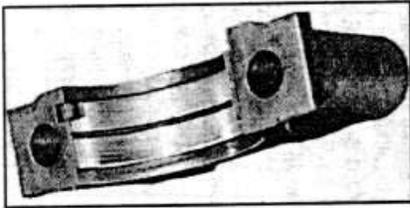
Е.31. Вкладыш 1. коренного подшипника коленчатого вала больше, чем вкладыши остальных подшипников, и имеет масляную канавку.
